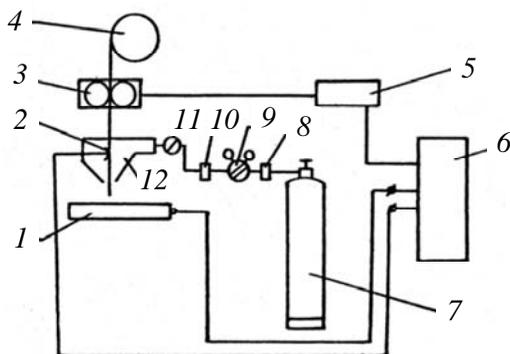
Схема поста для сварки (наплавки) в среде углекислого газа и смесях защитных газов:
